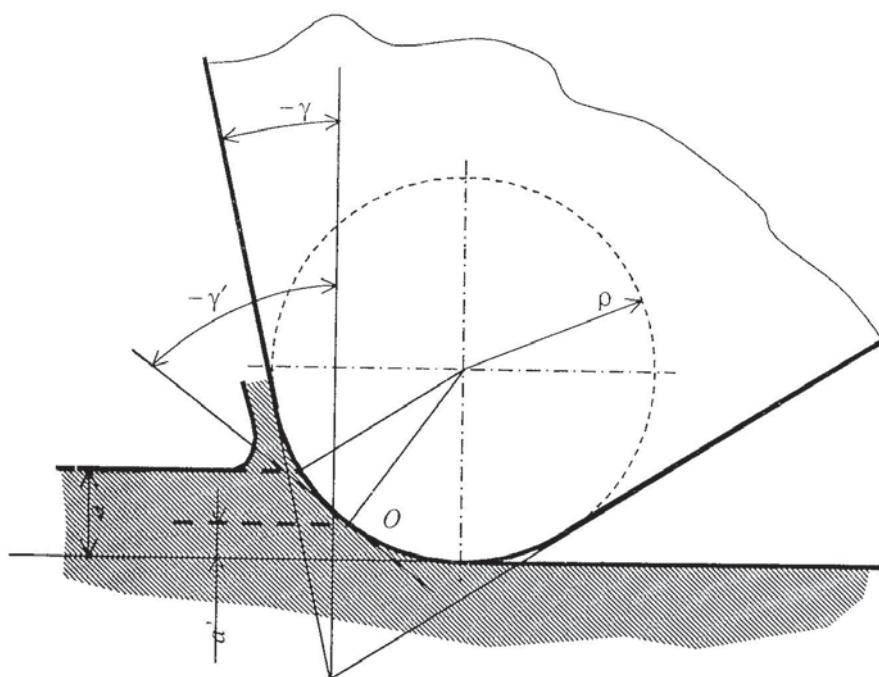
Схема взаимодействия с обрабатываемой поверхностью абразивного зерна, имеющего закругление кромки
